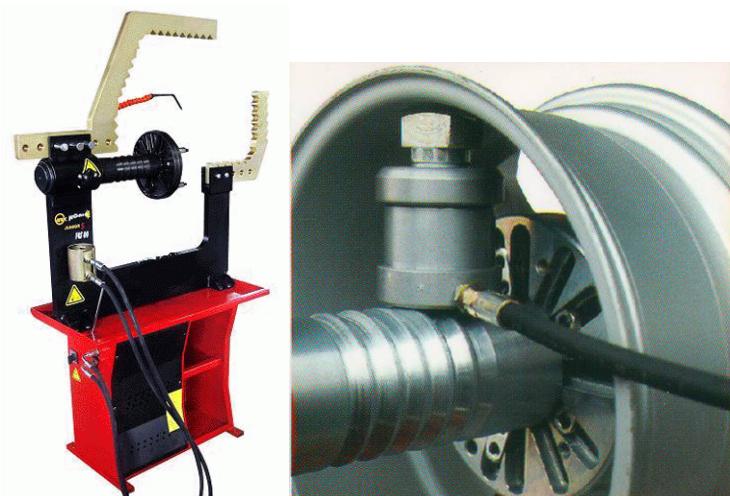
Общий вид станка и правка литого диска гидроцилиндром
